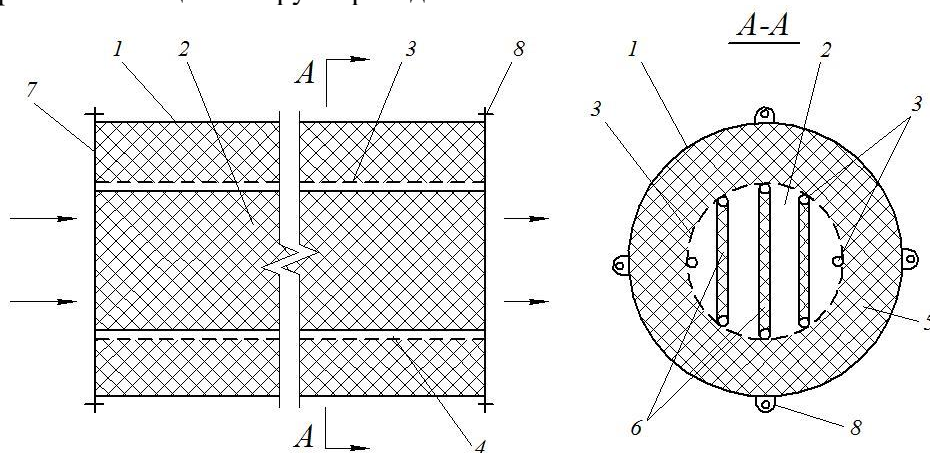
Глушник шуму осьового вентилятора: 1 – кожух зовнішнього циліндра; 2 – внутрішній циліндр; 3 – пластикова сітка; 4 – ребра жорсткості; 5 – звукопоглинальний шар; 6 – вертикальні рамки; 7 – фланці; 8 – провужини
